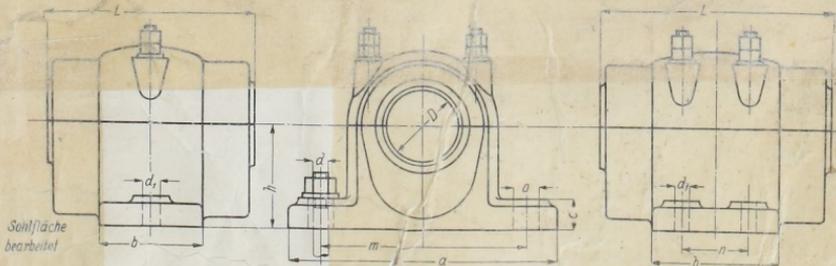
Stehlager nach DIN 118; links mit zwei, rechts mit vier Fußschrauben. Vgl. Zusammenstellung 133.
